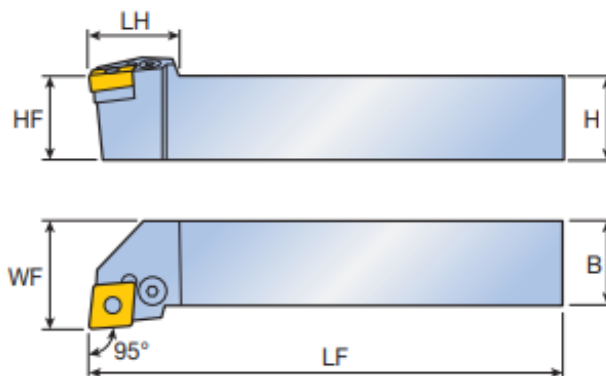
Державка PCLNR3232 P1906D [7, с. 59]
